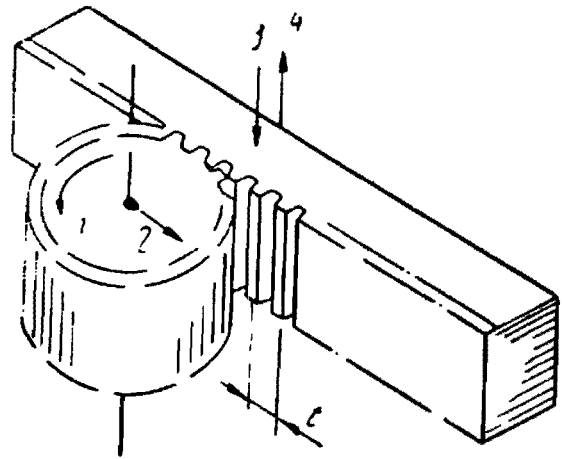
Схема для уяснения сущности нарезания зубчатого колеса гребенкой на станке типа Мааг
